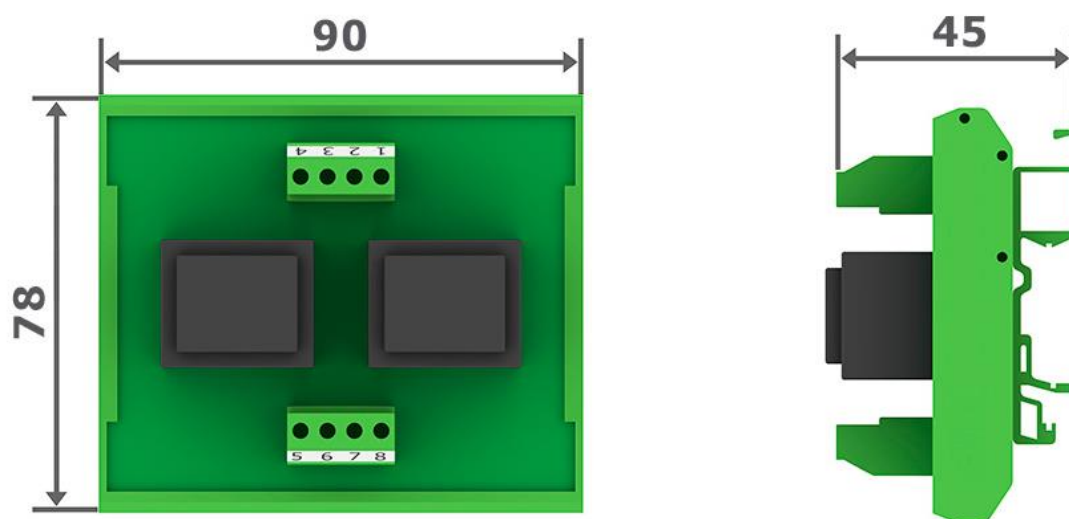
Габаритные и установочные размеры YCO – U
